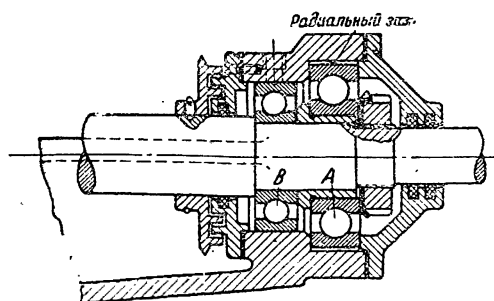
Комбинированный упорный и радиальный подшипник для одностороннего давления.
